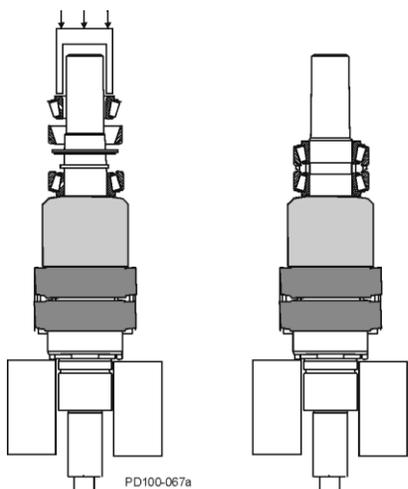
Ensemble roulement à rouleaux coniques arrière
